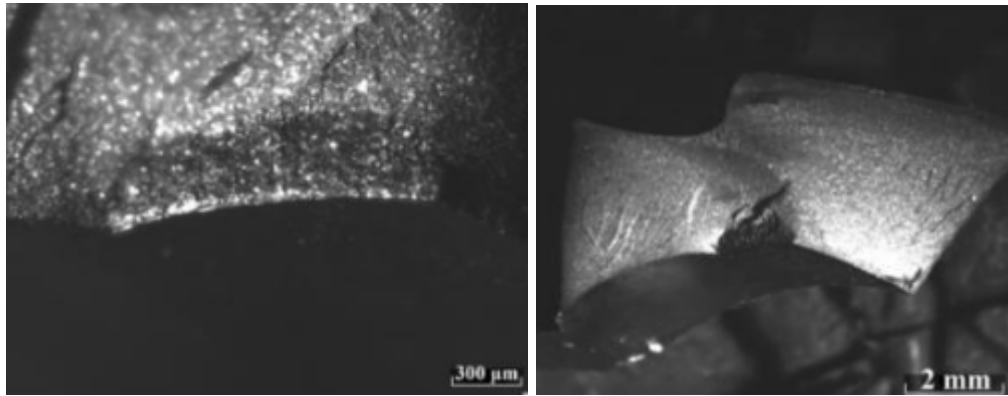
Злам 2. Поверхня зовнішньої обойми підшипника № 7
